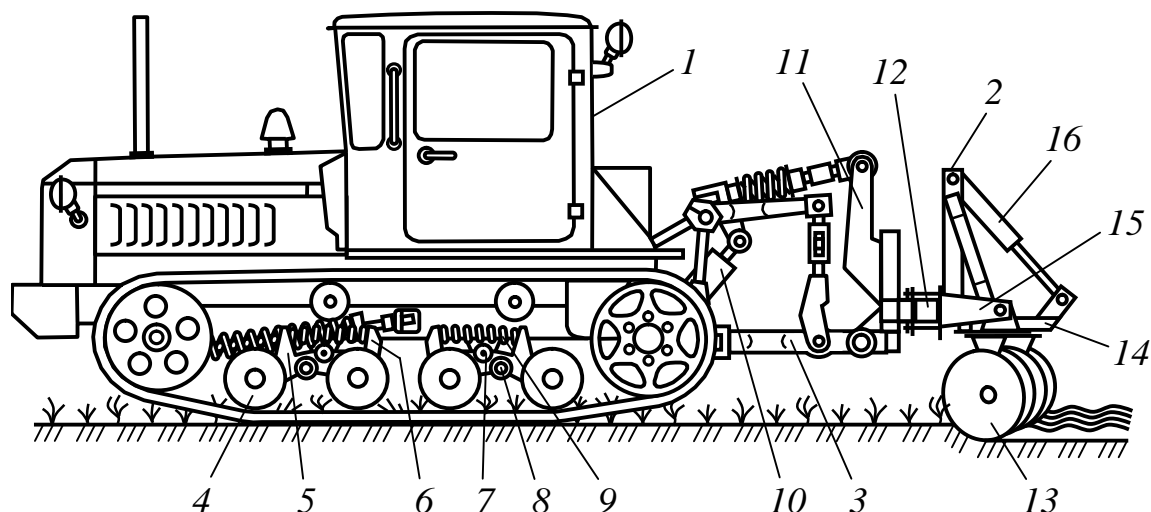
Общий вид и исследуемые элементы почвообрабатывающего агрегата: 1 – трактор; 2 – лесной дисковый культиватор с гидравлическим предохранителем; 3 – звенья механизма навески трактора; 4 – опорный каток; 5 и 6 – внешний и внутренний балансиры каретки; 7 и 8 – оси качания внутреннего и внешнего балансиров; 9 – пружина; 10 – гидроцилиндр навесного механизма; 11 – автоматическая сцепка; 12 – рама культиватора; 13 – дисковая батарея; 14 – поворотная стойка дисковой батареи; 15 – рамка дисковой батареи; 16 – гидроцилиндр предохранителя культиватора
